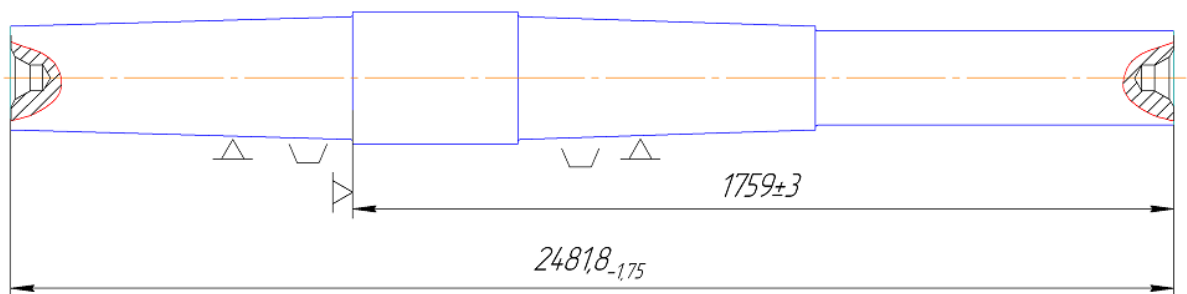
Базування валу на свердлильній та розточній операції
